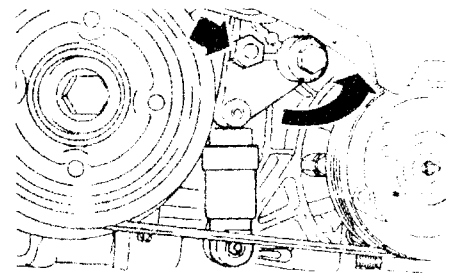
Montaje de la correa de accesorios (motores X20D)
